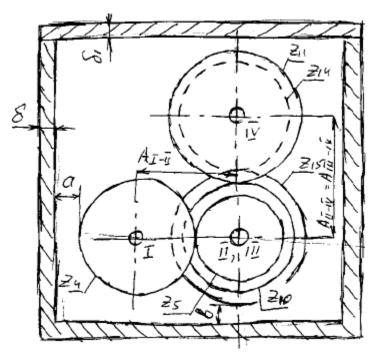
Эскизная компоновка свертки коробки скоростей.
